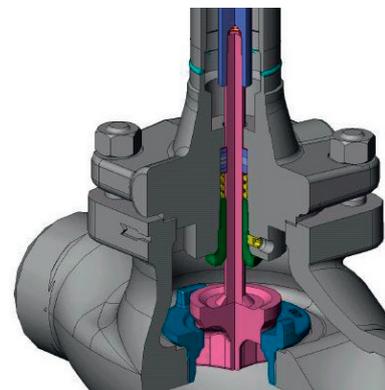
Ventil Typ 3246 mit Zirkulationssperre
